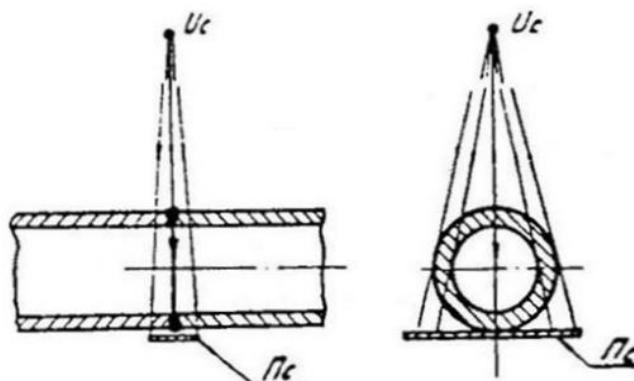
Схема фронтального просвечивания через две стенки за одну установку для соединения труб
